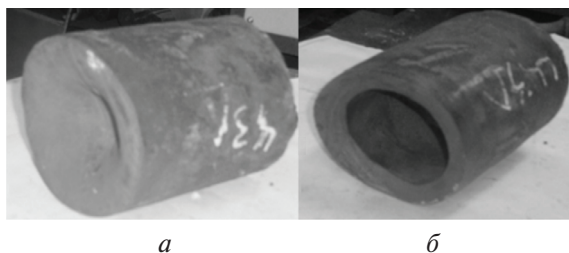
Фото задних концов обжатой заготовки и гильзы (заготовка с плоским торцом)
